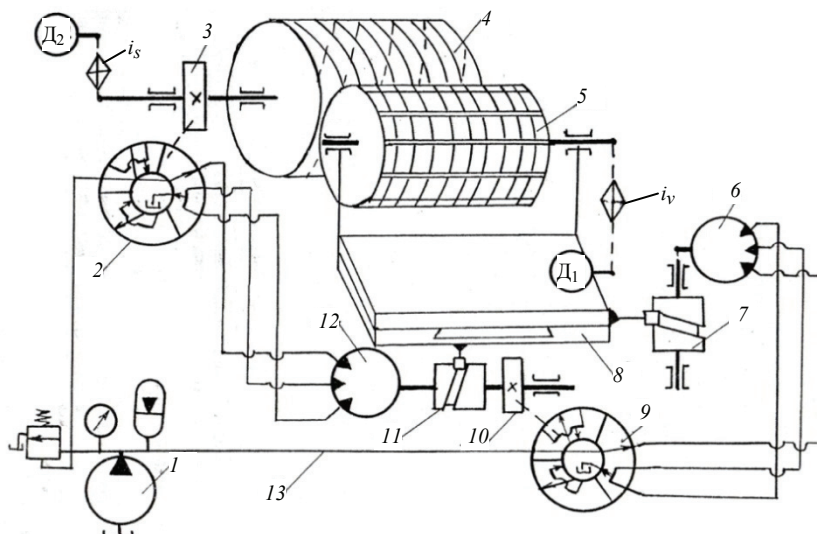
Структурная схема резбифрезерного станка с гидравлическими внутренними связями в кинематических цепях продольной и поперечной подач для нарезания коротких резьб гребенчатыми фрезами
